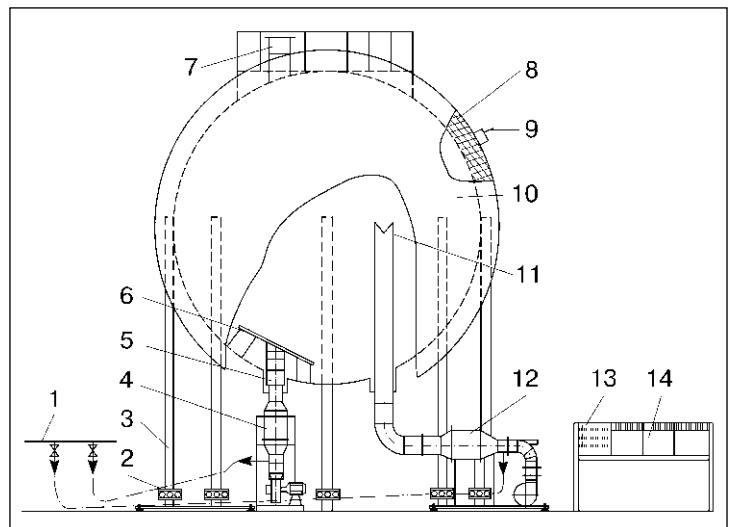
Схема поста для объемной термической обработки нагревом изнутри сферических резервуаров вместимостью 600 м³: 1 — газопровод; 2 — катковые опоры; 3 — стойки резервуара; 4 — теплогенераторная установка № 1; 5 — преобразователь потока; 6 — распределитель теплогенераторной установки № 1; 7 — дроссель; 8 — теплоизоляция; 9 — термоэлектрический преобразователь; 10 — сферический резервуар; 11 — распределитель теплогенераторной установки № 2; 12 — теплогенераторная установка № 2; 13 — милливольтметр 4500; 14 — автоматические регистрирующие потенциометры КСП-4
